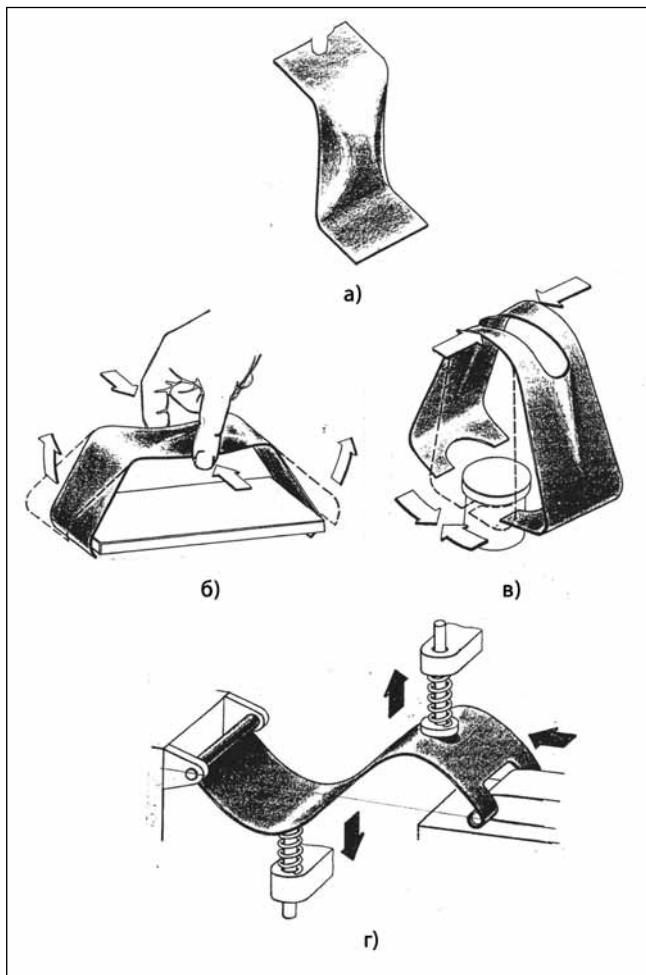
Упругодеформируемые механизмы: а) передача с противоположными плечами, б) захват, в) грейферныйхват, г) ленточная передача поступательного движения
